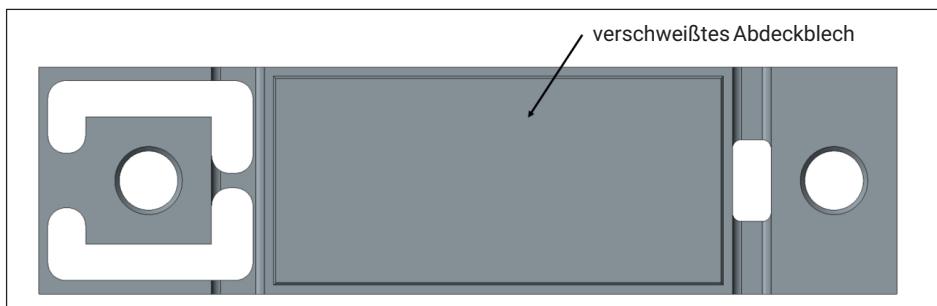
Hermetisch verschweißtes Abdeckblech auf der Oberseite des Aufnehmers
